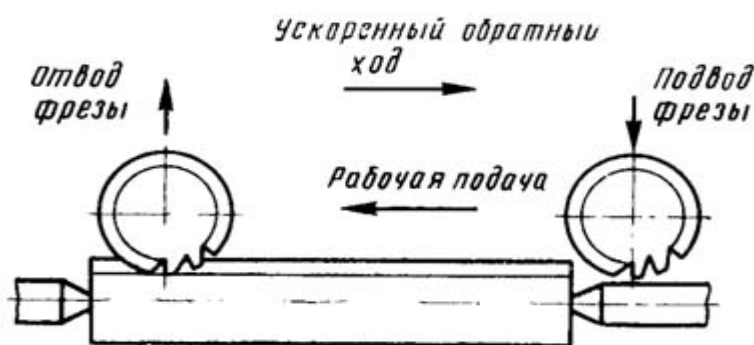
Автоматический цикл шлицефрезерного станка 5350А
